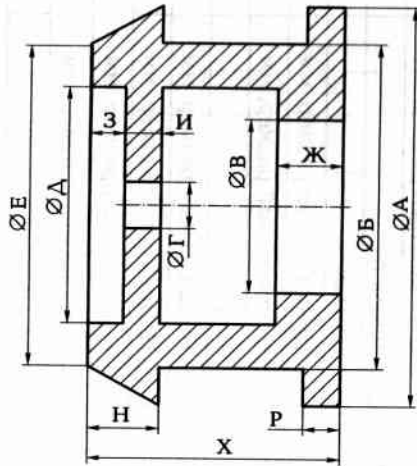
Эскиз обрабатываемого диска к заданию 3.6
